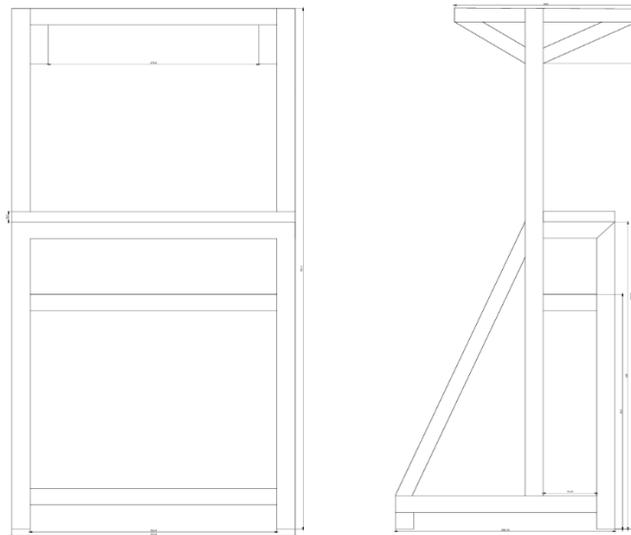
Dimensión de la estructura. Fuente: CAD.
